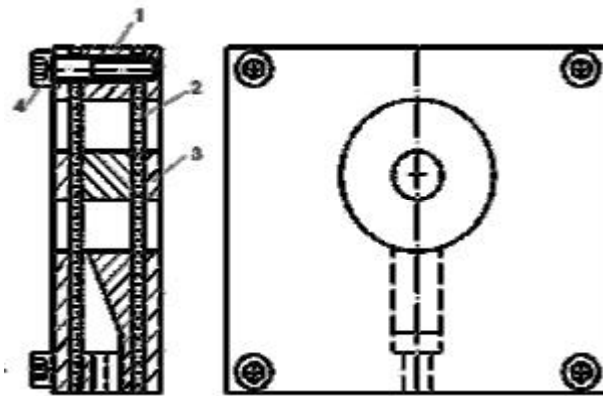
Matrita. 1- placa activa; 2- ecran; 3- placa de fixare; 4- surub de fixare.
